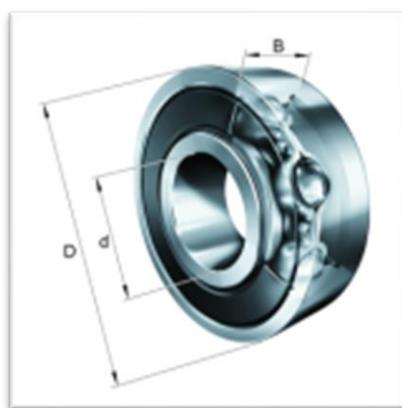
Rodamiento bolas SCHAEFFLER dimensiones principales
